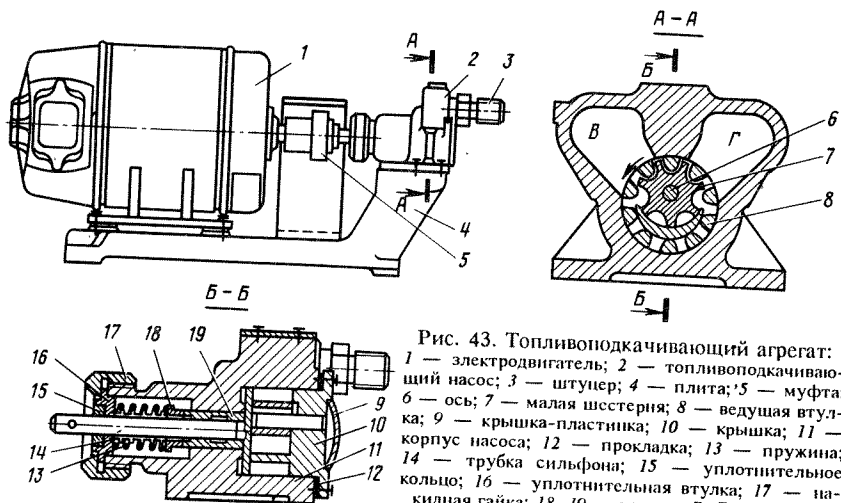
Топливоподкачивающий агрегат: 1 — электродвигатель; 2 — топливоподкачивающий насос; 3 — штуцер; 4 — плита; 5 — муфта; 6 — ось; 7 — малая шестерня; 8 — ведущая втулка; 9 — крышка-пластинка; 10 — крышка; 11 — корпус насоса; 12 — прокладка; 13 — пружина; 14 — трубка сильфона; 15 — уплотнительное кольцо; 16 — уплотнительная втулка; 17 — накидная гайка; 18, 19 — втулки; В, Г — полости
